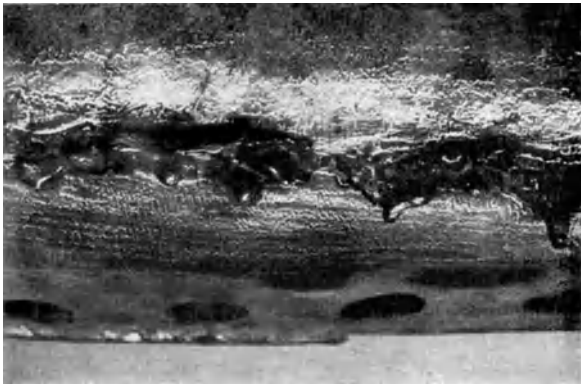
Größere Teilaufnahme der Rückseite des geschweißten Risses R_2 (Draufsicht).
